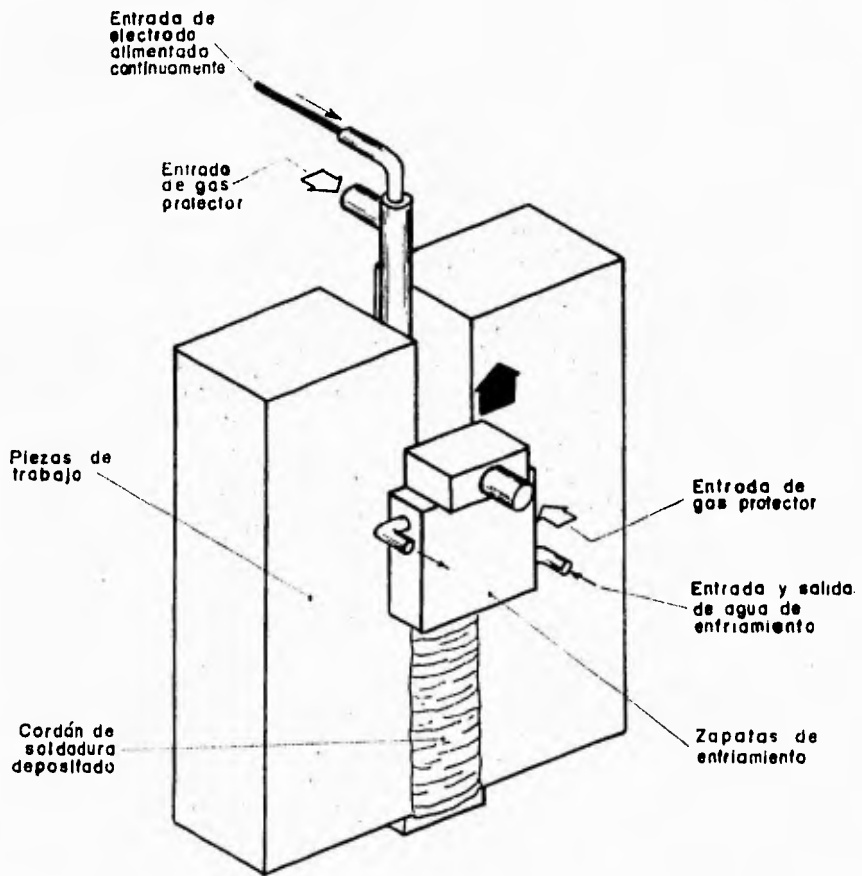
Soldadura por electrogas (EGW)
